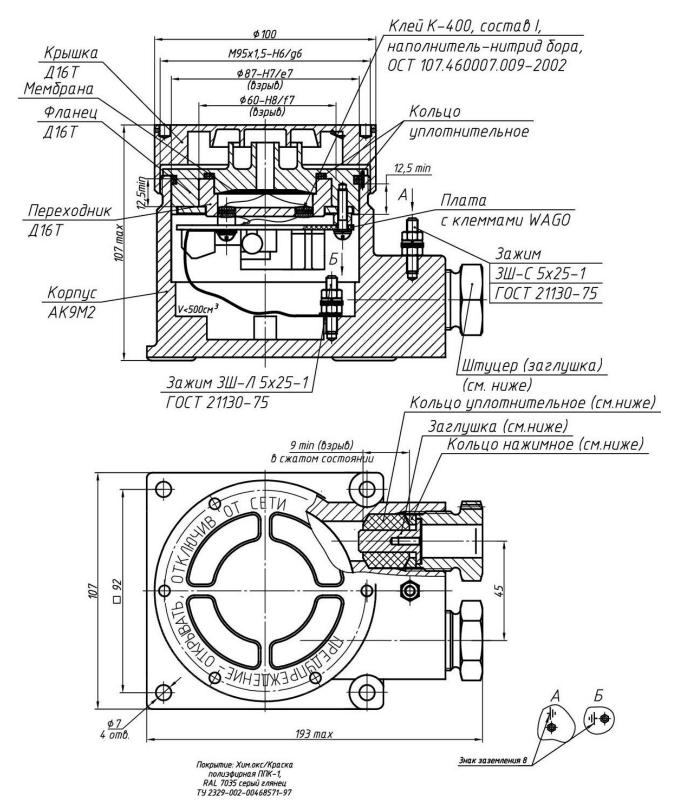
а - Габаритный чертёж звуковых оповещателей повышенной мощности ExOППЗ-2В-ПМ-А и ExOППЗ-2В-ПМ-220-А в алюминиевом корпусе (вариант), совмещённый с чертежом взрывозащиты. Маркировка показана в п. 1.6
